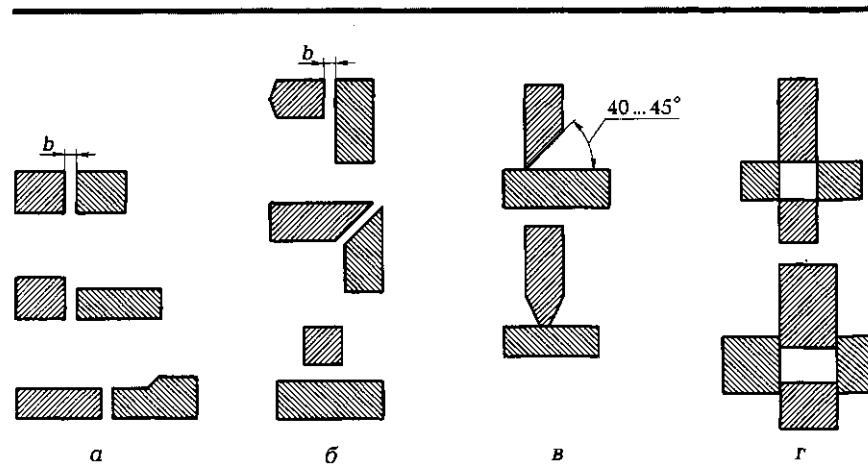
Типы соединений, выполняемых электрошлаковой сваркой:
